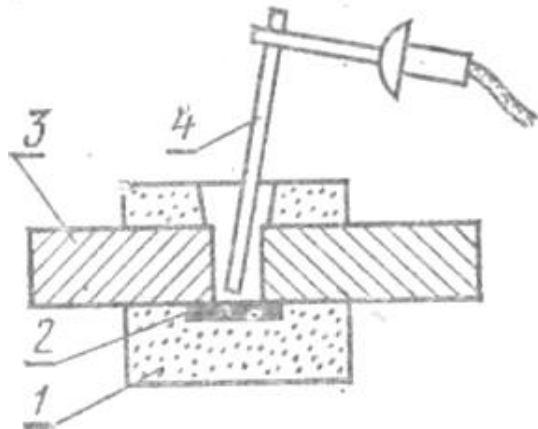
Гаряче зварювання чавуну: 1 - формувальна земля, 2 - графітна пластинка; 3 - зварювані деталі, 4 - електрод.
